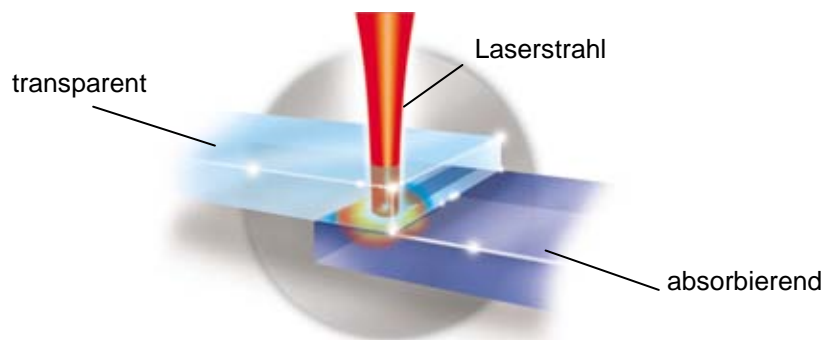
Prinzipskizze Laser-Durchstrahlschweißen von Kunststoffen
